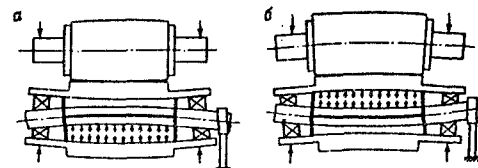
Принцип действия двухкамерного валка ВК:
